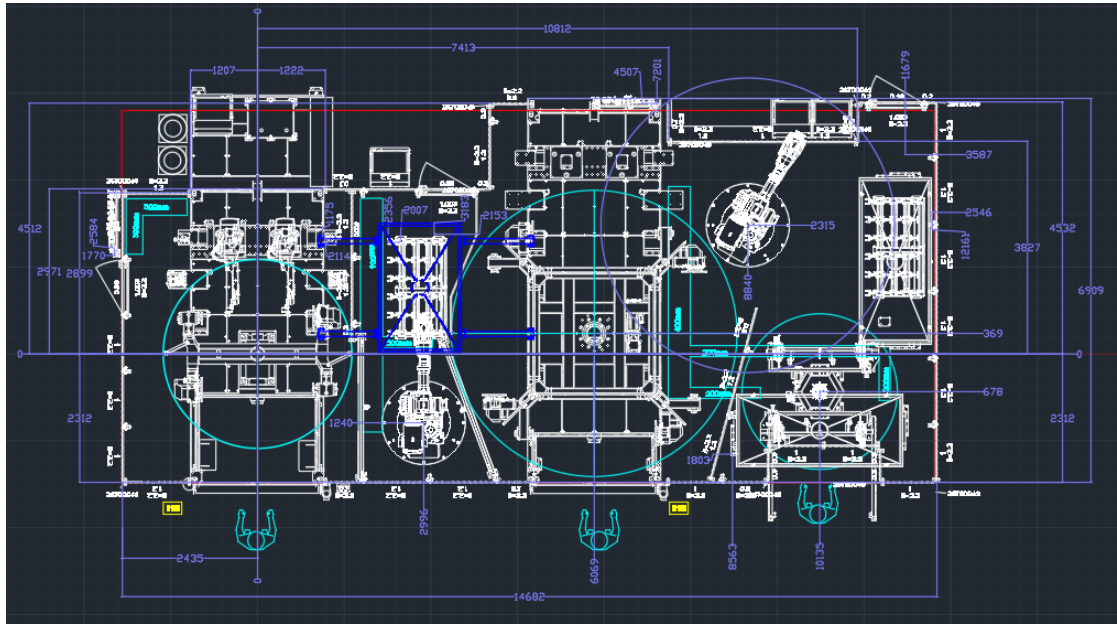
Layout de nuestra instalación. El utillaje OP10 está instalado en el posicionador de la izquierda. Fuente: Interob (2016).
